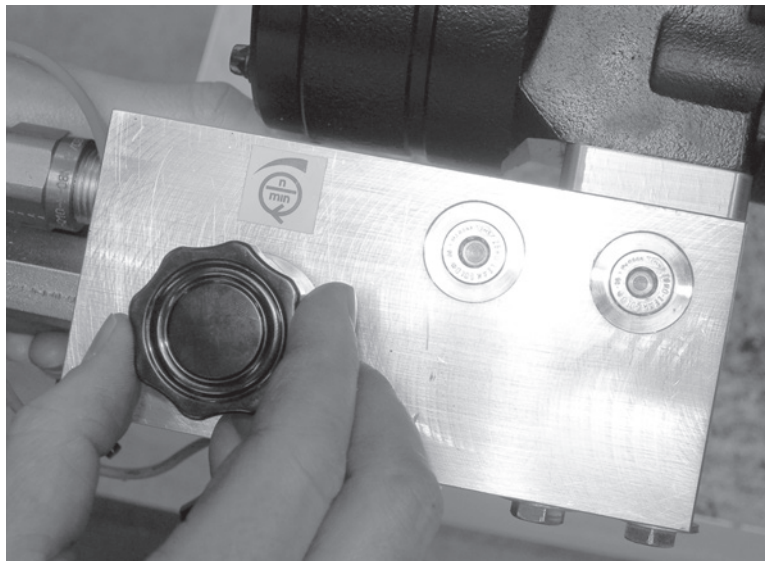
Utilizzare il selettore di velocità sul collettore idraulico per regolare la velocità di rotazione della macchina.
